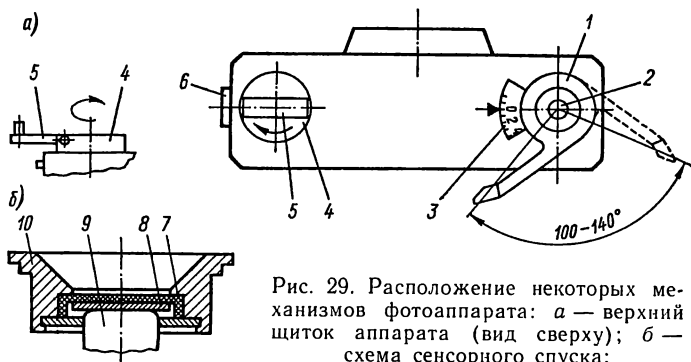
Расположение некоторых механизмов фотоаппарата: *а* — верхний щиток аппарата (вид сверху); *б* — схема сенсорного спуска:
